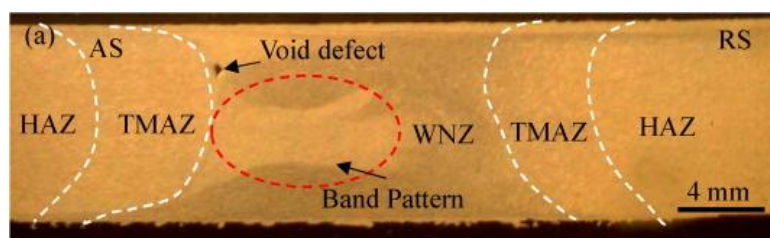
Soudure par BT-FSW d'un alliage 6061-T6 [14]
